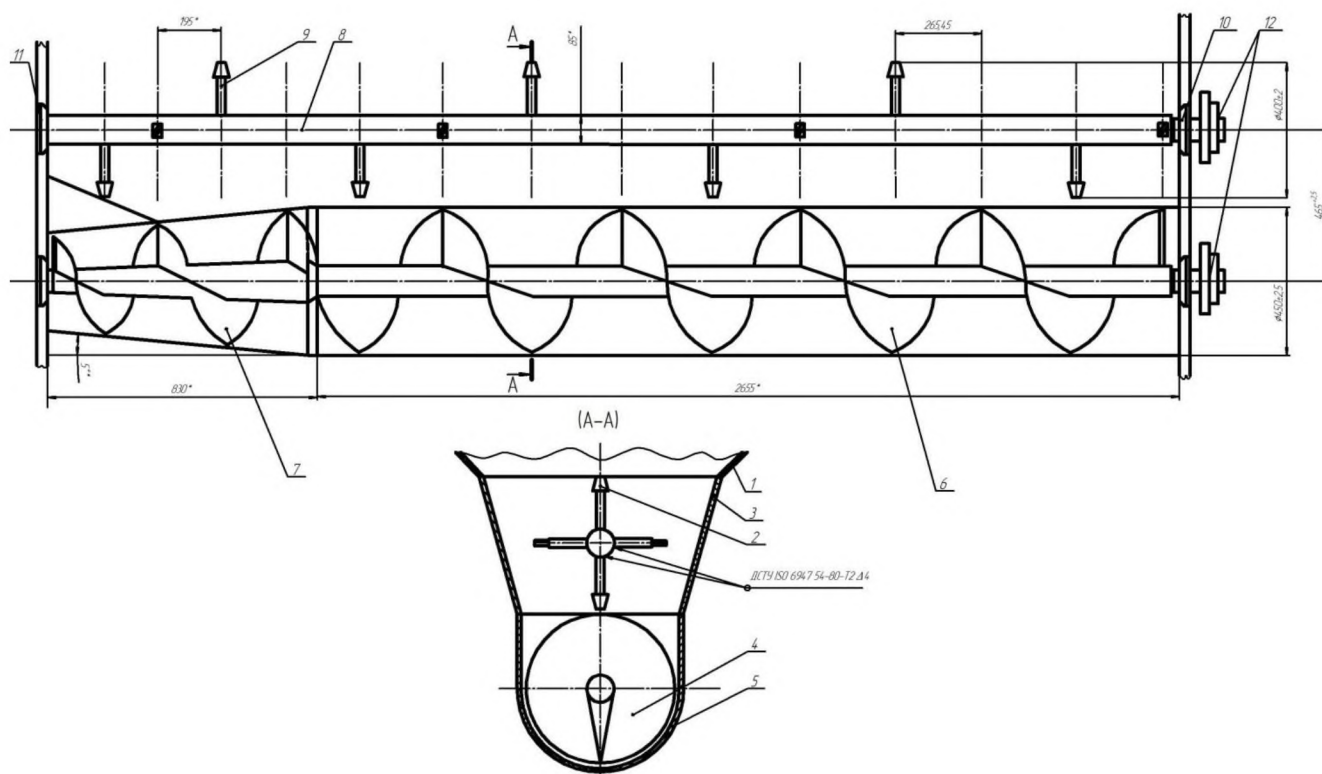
Конструктивне компонування пристрою подачі органічних добрив: 1- секція бункера; 2- розрихлювач; 3- конусний корпус; 4- шнек; 5- корпус шнека; 6- циліндрична частина шнека; 7- конічна частина шнека; 8- вал розрихлювача; 9- зубові лопатки; 10 і 11- підшипникові вузли; 12- блок зірочок
